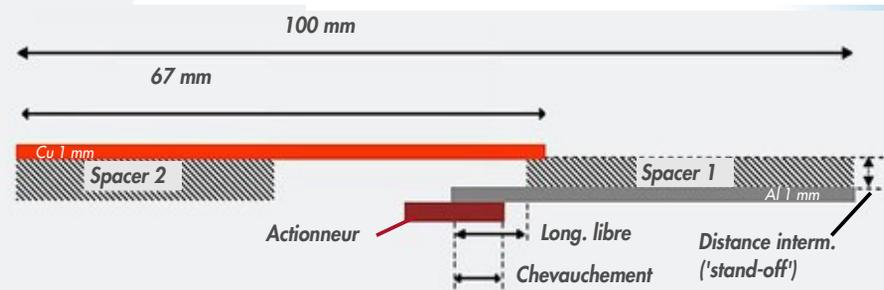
bobine plate, utilisée pour le soudage par impulsion électromagnétique de pièces sous forme de tôle (source: Institut Belge de la Soudure)
